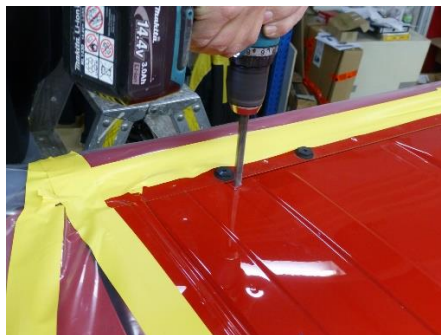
Dachausschnitt / roof cut-out [A0003929]
